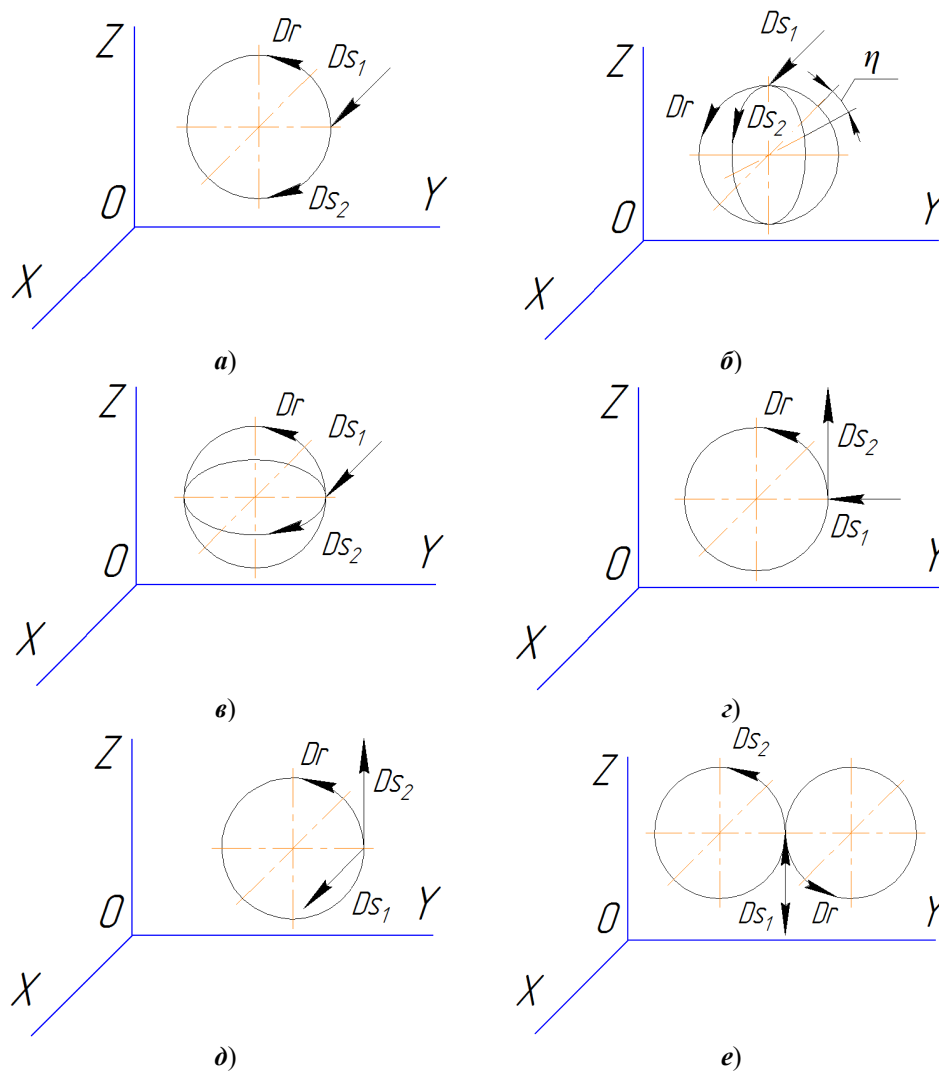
Кинематические схемы резания: а – обработка охватывающими фрезами (зенкерами) цилиндрической или конической поверхности; б, в – обработка охватывающими фрезами (зенкерами) неполной сферической поверхности; г – обработка с врезанием фрезы по дуге уступа или полузакрытой полости; д – обработка с врезанием фрезы по касательной плоской поверхности детали; е – обработка с врезанием фрезы по касательной плоской и цилиндрической поверхностями детали
